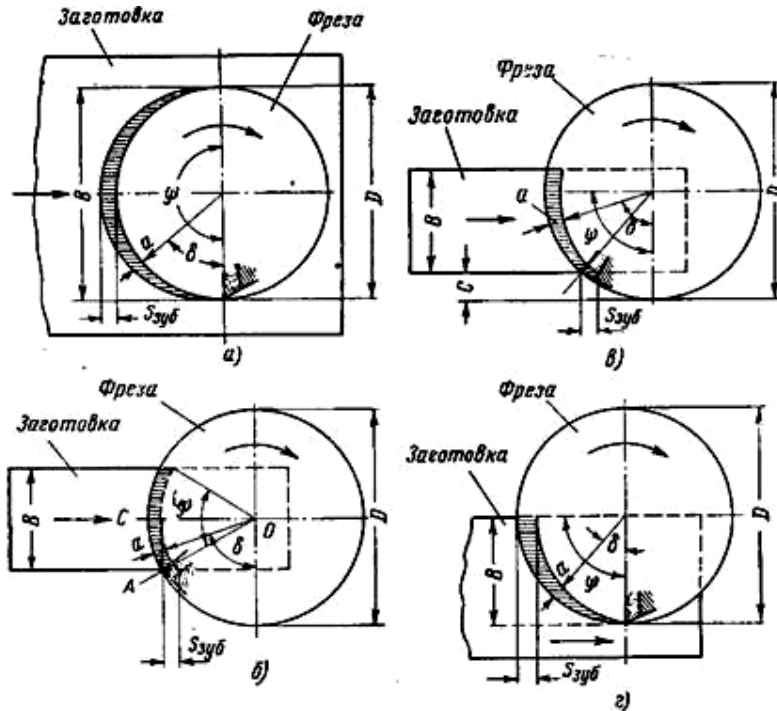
Форма стружки при фрезеровании торцевой фрезой:
